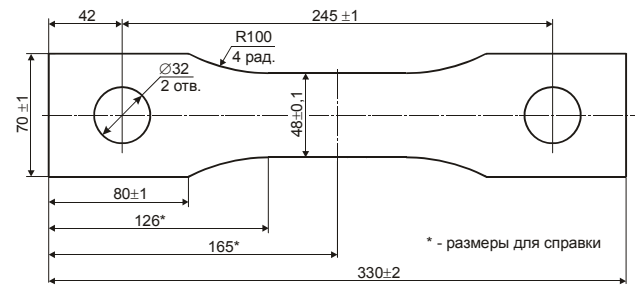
Геометрические размеры заготовки для изготовления образцов полос
